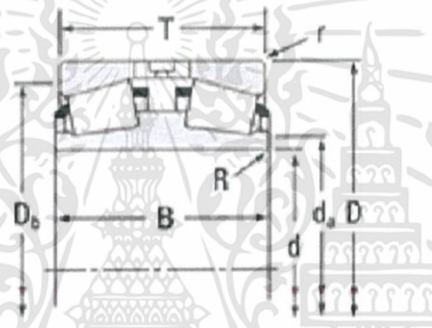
Dimensions Bearing SKF Explorer 23226 CC/W33
